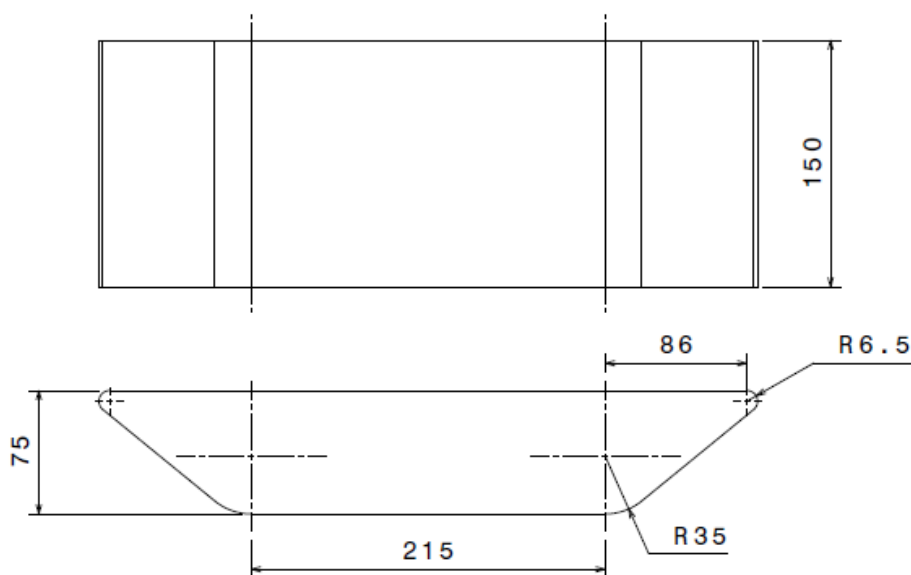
Geometria e dimensões do deslizador ou patim.
